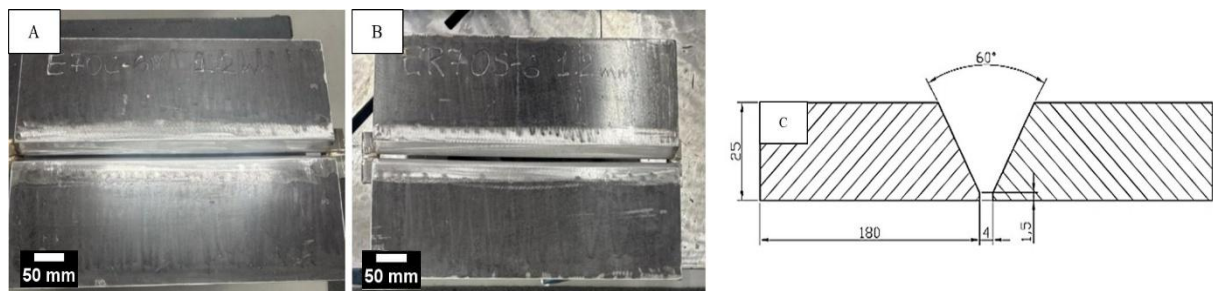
Corpos de Prova Consumível ER70S-6 (A), E70C-6M (B), Croqui da junta de soldagem (C).
